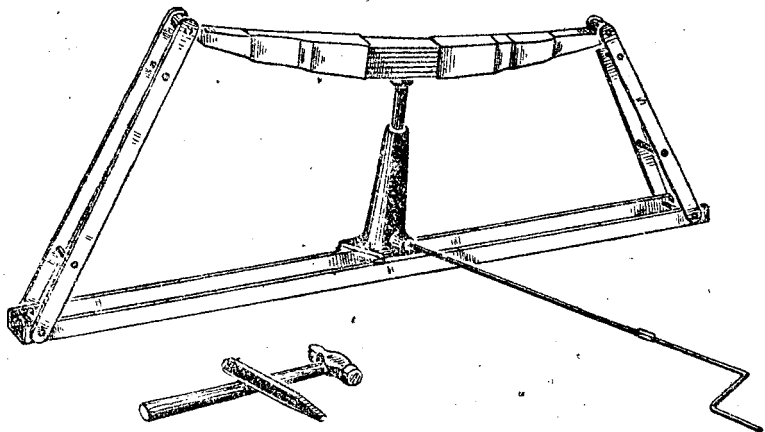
Специальное приспособление для выпрямления рессоры при надевании чехлов.
